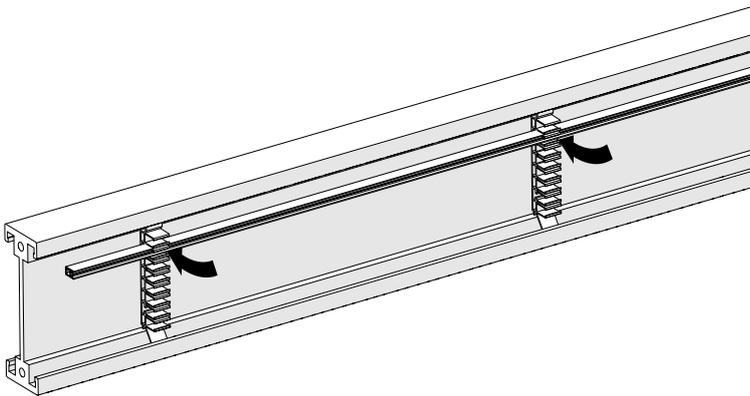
Tragprofil mit einer montierten Schleifleitungsschiene
